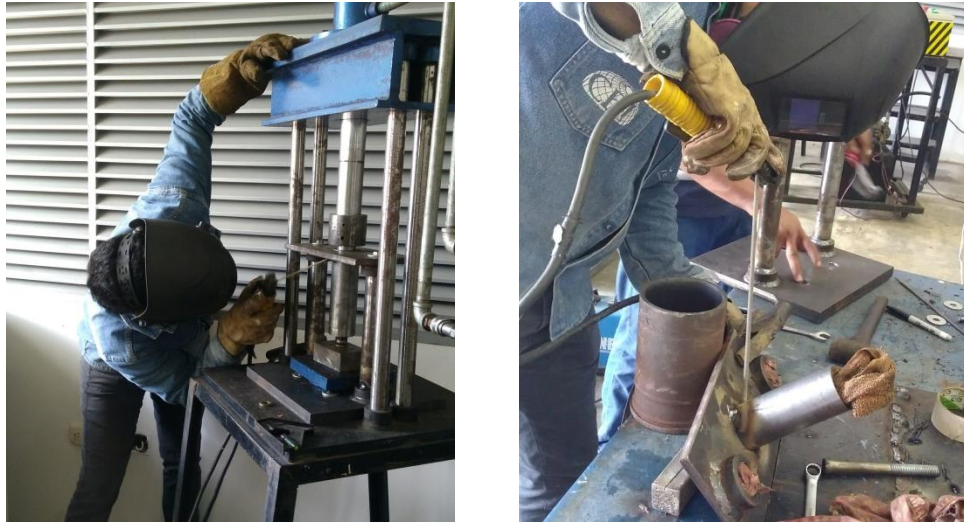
Proceso de soldadura para fijación del cilindro de plastificación a la placa superior.
